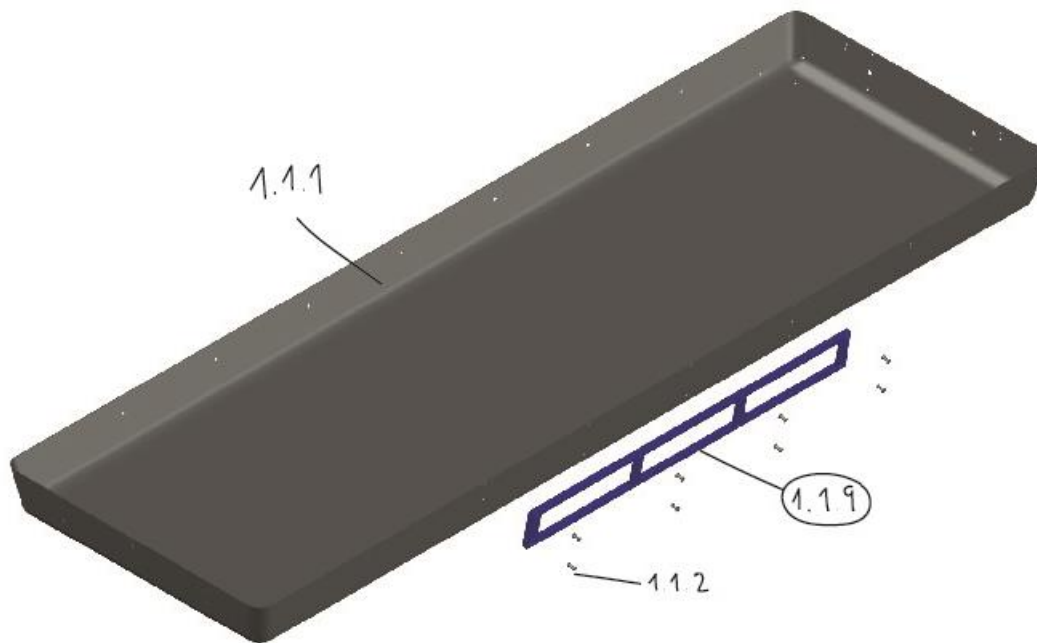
Explosionado de relaciones pieza 1.1.9
